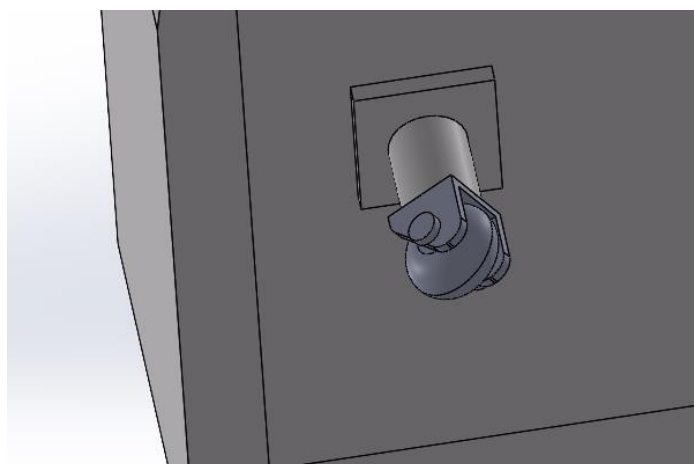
Widok po skosie od boku obrazujący ruch górnej części robota.
